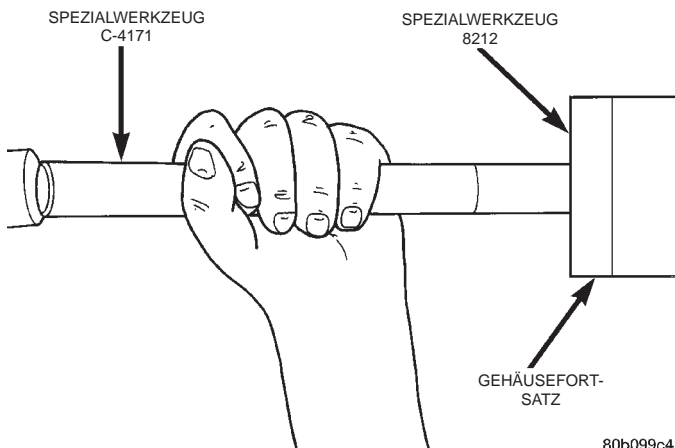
Wellendichtring in Gehäusefortsatz ausbauen
